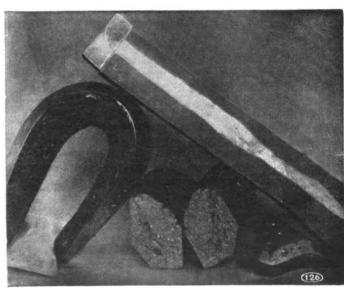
Proben von Spurkranzschweißung. M. 1:3.
